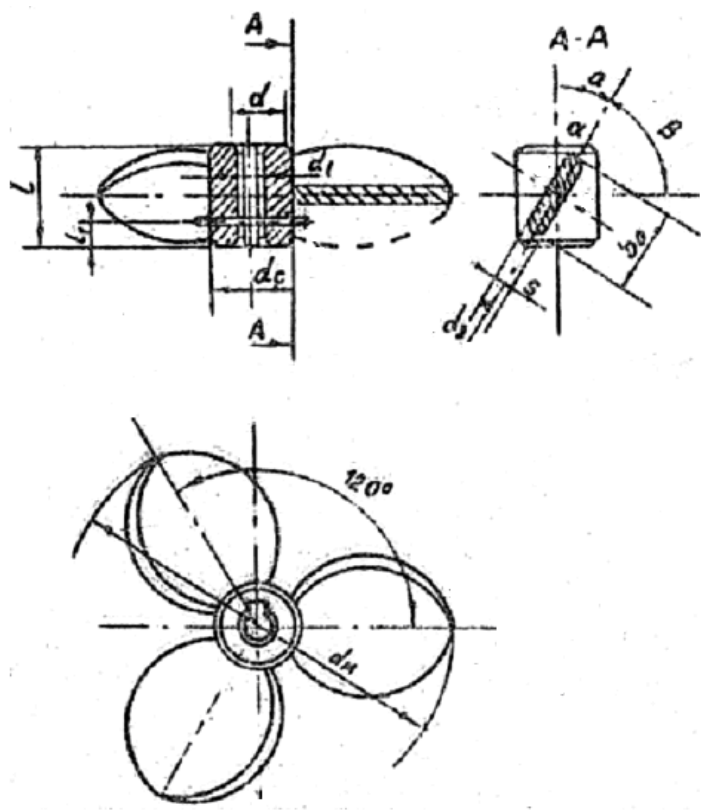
Типовая сварная конструкция трехлопастного перемешивающего устройства
